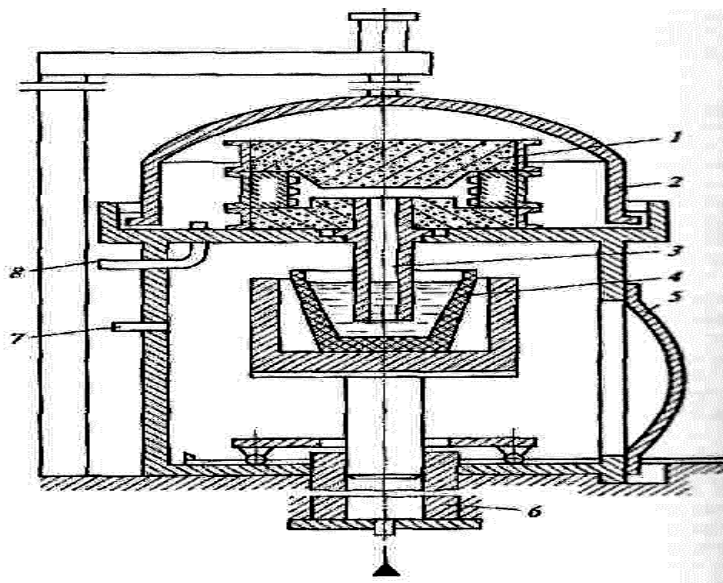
Схема установки для вакуумно-компрессорного литья 1 — форма; 2 — стальной колпак; 3 — металлопровод; 4 — тигель с расплавом; 5 - крышка нижней камеры; 6 — гидроцилиндр подъема тигля с расплавом; 7, 8 — трубопроводы пневмосистемы установки
